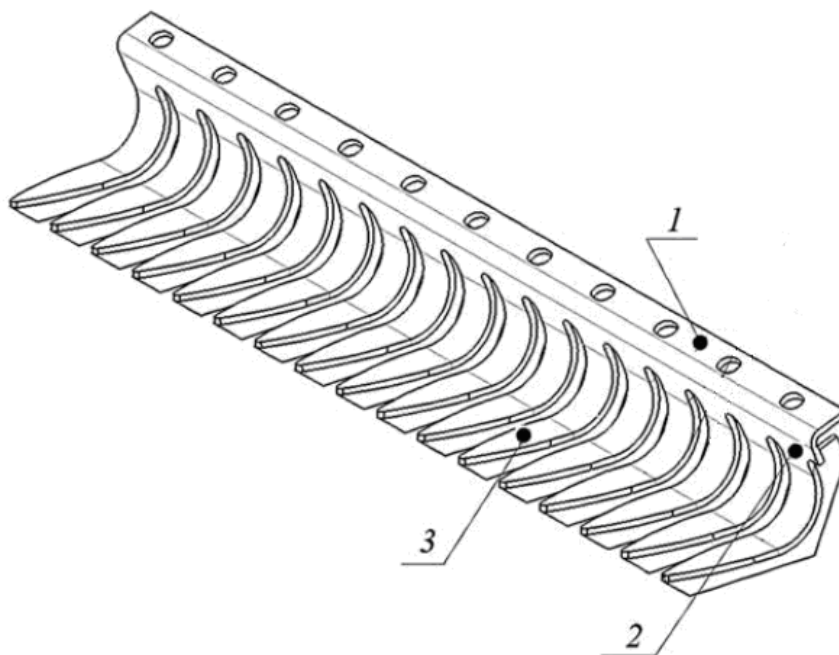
Гребінка для великонасінних культур: 1 – пластина; 2 – робоча поверхня; 3 – зуб.
